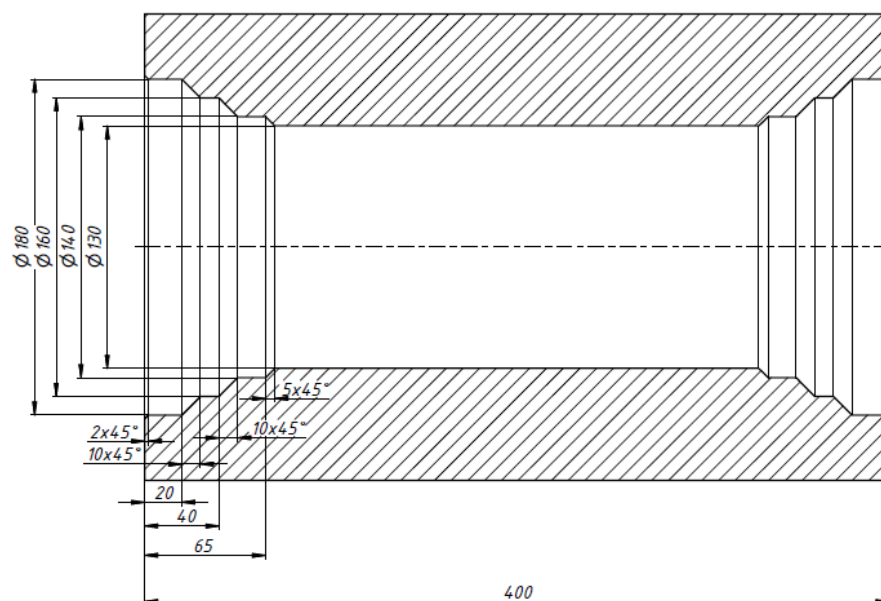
Ескіз поверхні обробленої заготовки
